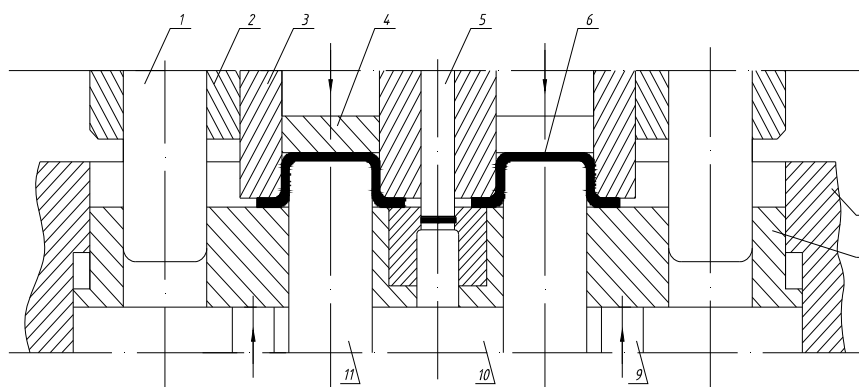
Штамп совмещенного действия для изготовления двух деталей (продольный разрез)
